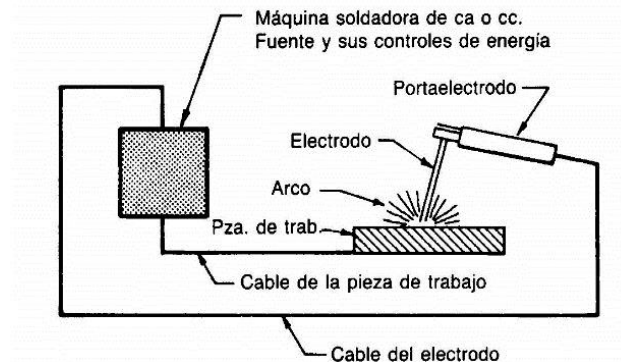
Esquema de soldadura por arco eléctrico
